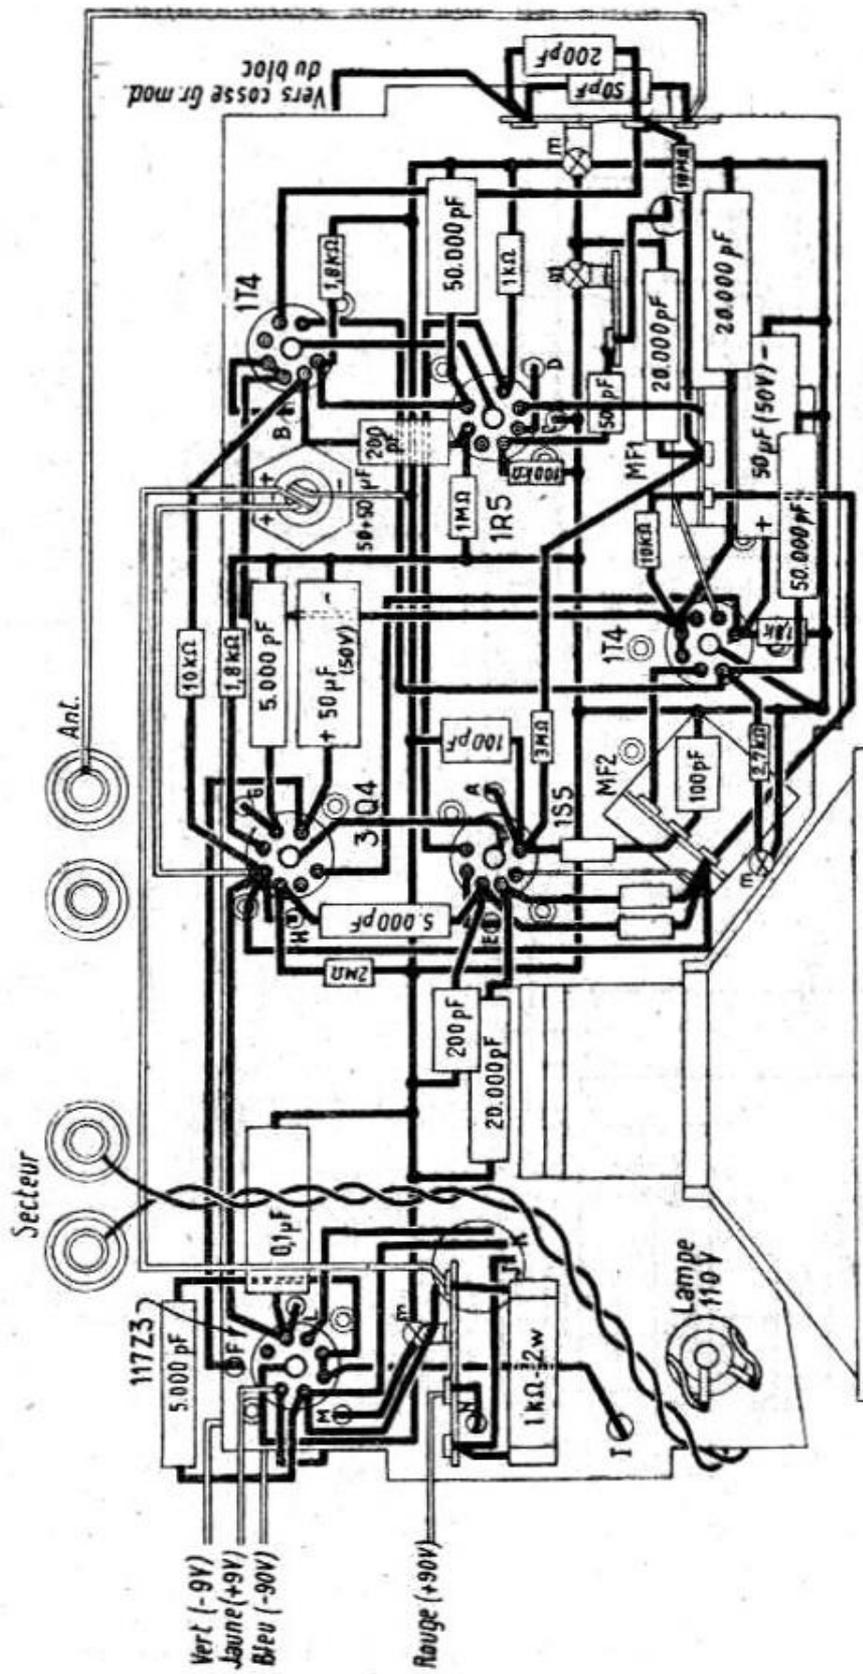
Câblage du « WEEK-END » sous le châssis
